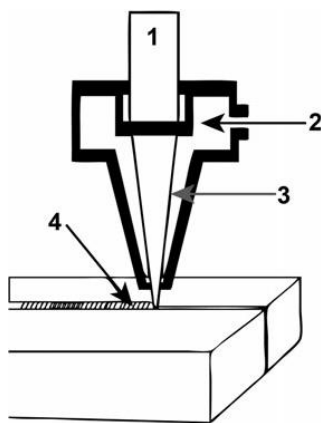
Esquema do processo de LBW. 1- Fonte emissora do laser, 2- sistema ótico, 3- bocal de saída do laser e do gás protetor, 4- junta de soldadura [42].
